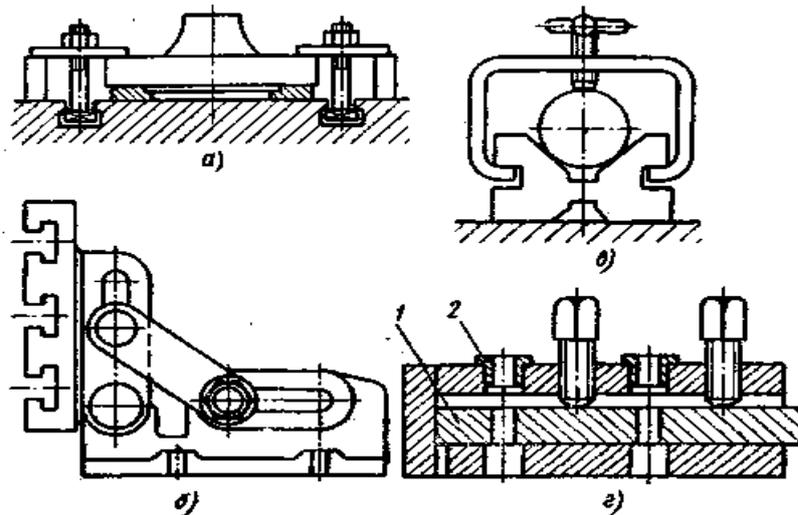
Приспособления для закрепления заготовок на сверлильных станках
